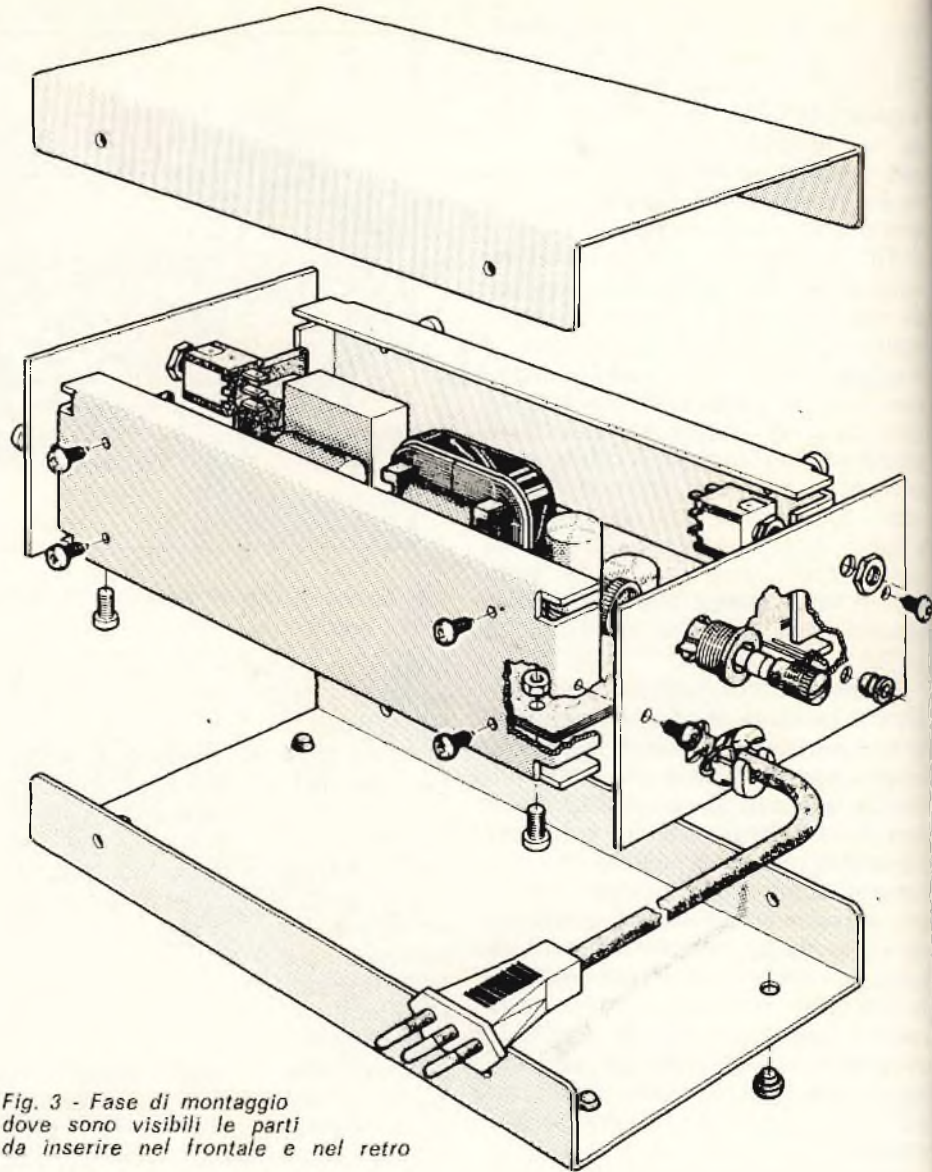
Fase di montaggio dove sono visibili le parti da inserire nel frontale e nel retro
